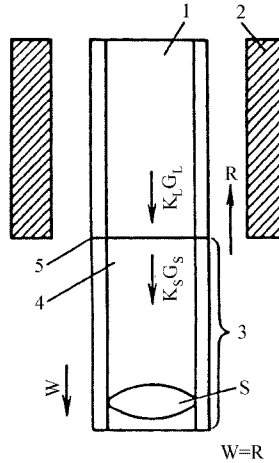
Схема процесса направленной кристаллизации цилиндрической отливки [169]:
